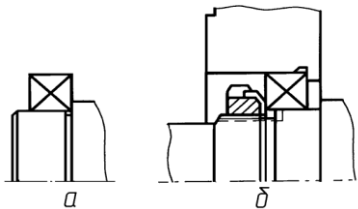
Кріплення підшипників за схемою «в розтяжку»: а – встановлення внутрішнього кільця підшипника з упором в бурт вала; б - шліцьовою гайкою зі стопорною багатолапчастою шайбою
